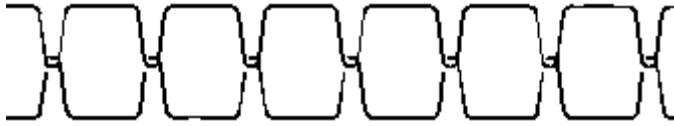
Строение двухниточной стачивающей строчки челночного стежка
